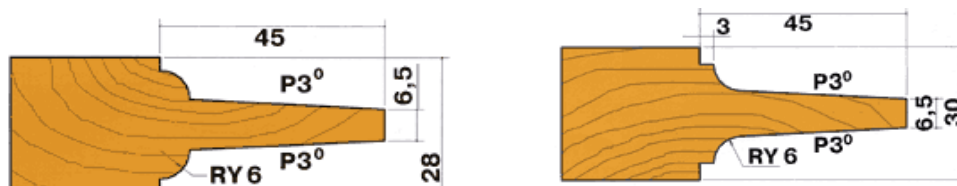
Фрезы концевые со сменными ножами для обработки криволинейных поверхностей
